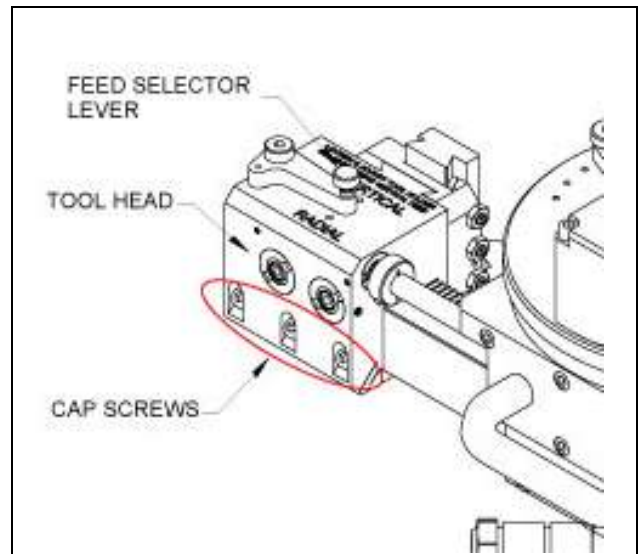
EMPLACEMENT DES VIS D'ASSEMBLAGE
